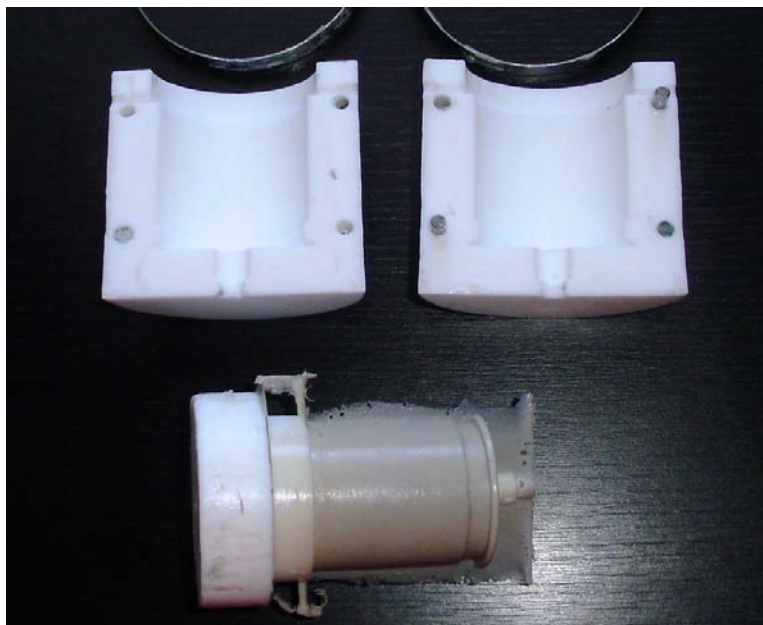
a) Příprava formování b) Odformovaný prototyp s uhlíkovou tkaninou
